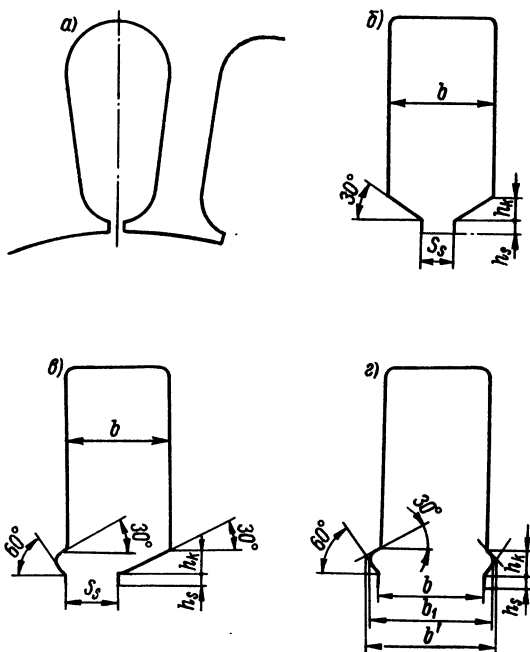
Форма пазов статора: а — овальный полузакрытый; б — прямоугольный полузакрытый; в — полуоткрытый; г — открытый
